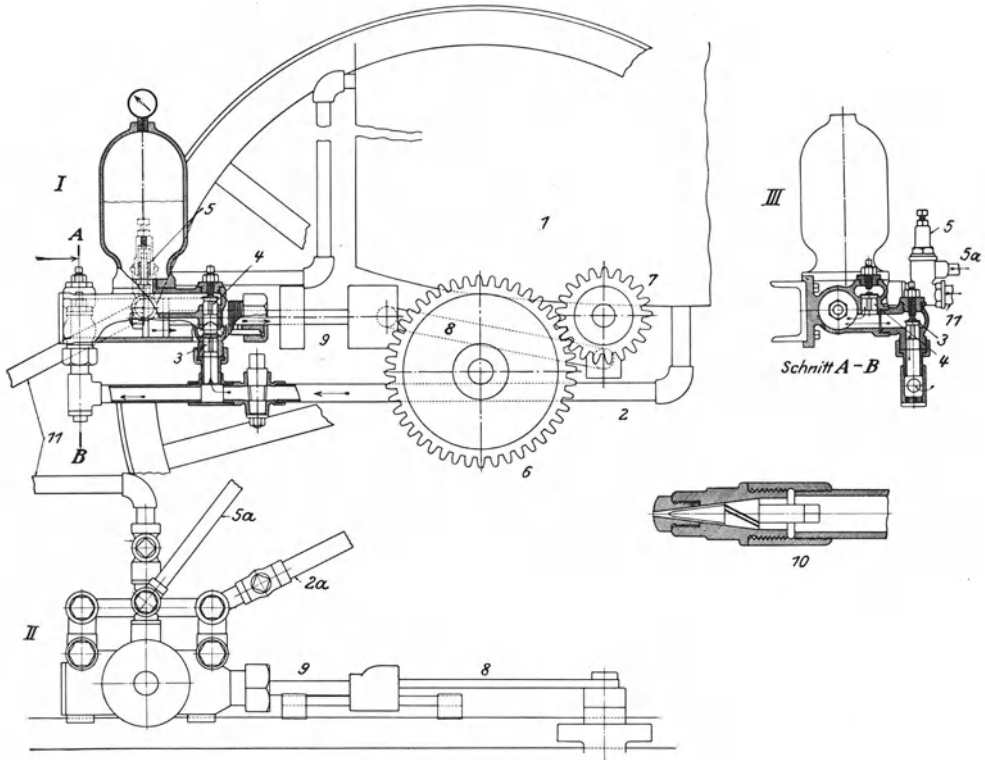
Schnitt einer fahrbaren Hederichspritze mit doppelwirkender Saug- und Druckpumpe. *I* Längsschnitt, von der Seite gesehen. *II* Längsschnitt von oben. *III* Schnitt A—B. 1 Behälter; 2 und 2 a Auslaufrohr des Behälters; 3 Saugventil; 4 Druckventil; 5 Sicherheitsventil; 5 a Ablauf zum Behälter; 6 Auswechslungsrads, an die Radachse gekuppelt; 7 Kupplungsrads; 8 Pumpenstange; 9 Pumpenstempel; 10 Verstäuber- mundstück; 11 Leitung zum Verstäuberrohr. Orig.-Zeichn.
